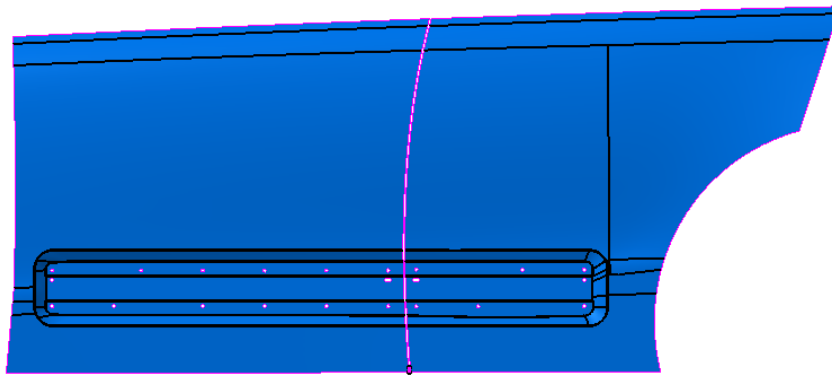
Paneles de puerta con fijaciones planteadas.
